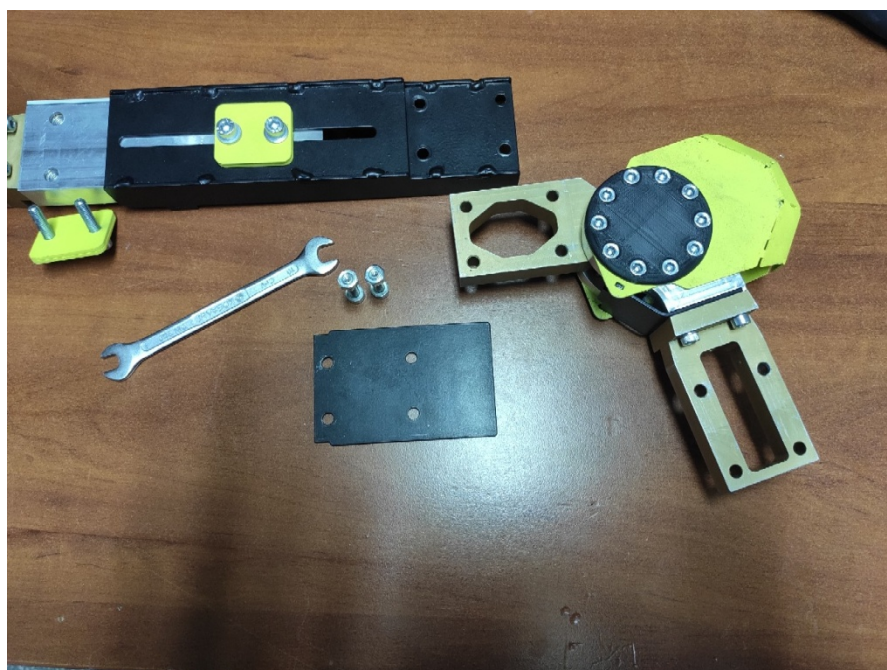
Отделение коленного шарнира от корпуса бедра
